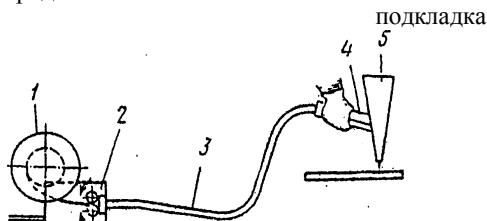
Полуавтоматическая дуговая сварка: 1 – кассета с электродной проволокой; 2 – механизм подачи электродной проволоки; 3 – гибкий шланговый провод; 4 – держатель (горелка); 5 – воронка для флюса
